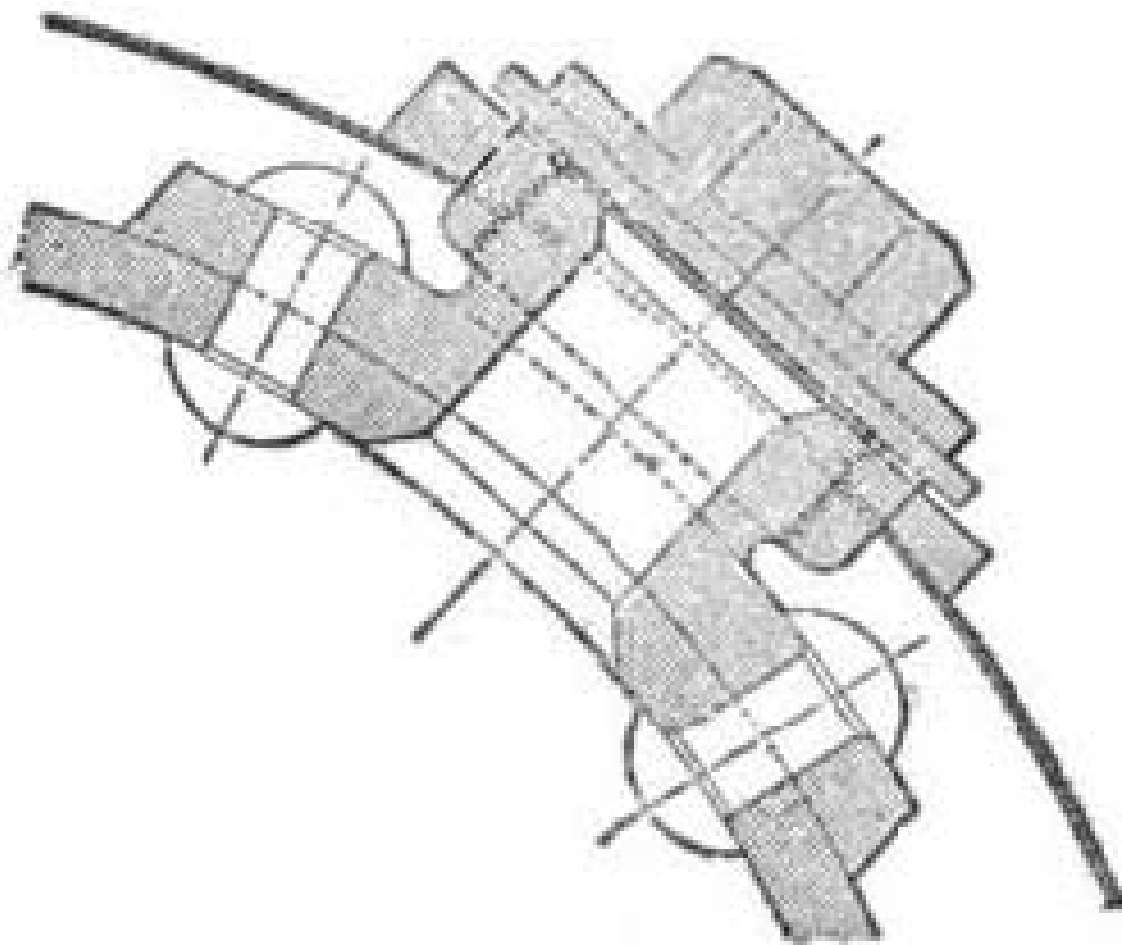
Boca de lavado montada sobre la parte redondeada de la caja de fuego, con tapón roscado exteriormente.
